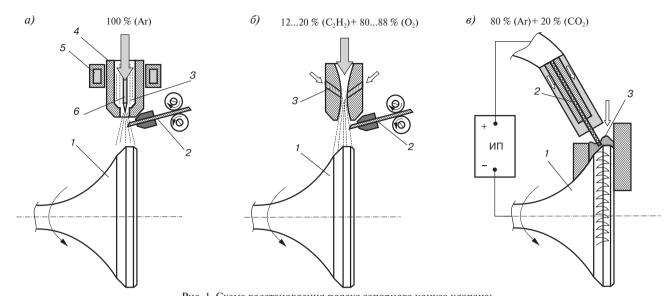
Схема восстановления пояска запорного конуса клапана: a — плазменное напыление: I — клапан; 2 — подача проволоки; 3 — подача шихты; 4 — анод; 5 — система охлаждения; 6 — катод; 6 — газопламенное напыление; 8 — электродуговая наплавка: 1 — клапан; 2 — подача проволоки; 3 — подача шихты. Π — импульсный преобразователь
